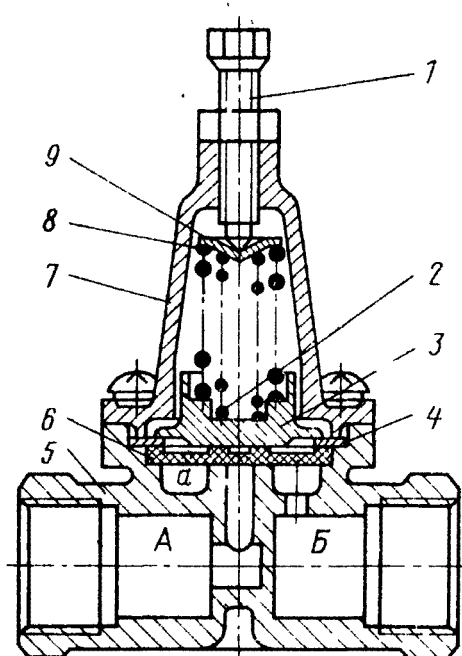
Одинарный перепускной защитный клапан (без обратного клапана):
